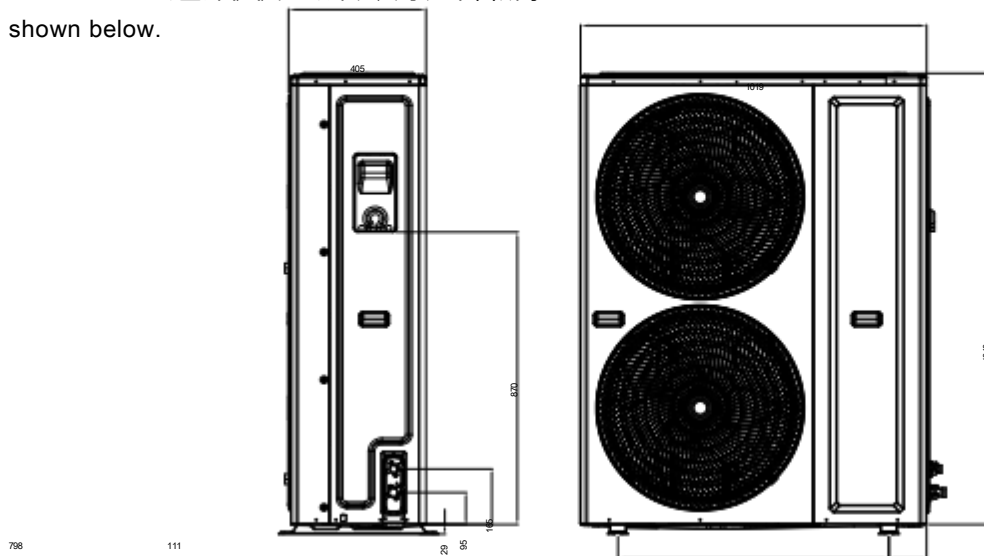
：12.5kw 外机外观尺寸图 Fig. 2-7: Outline Dimensions of 12.5kW Outdoor Unit
